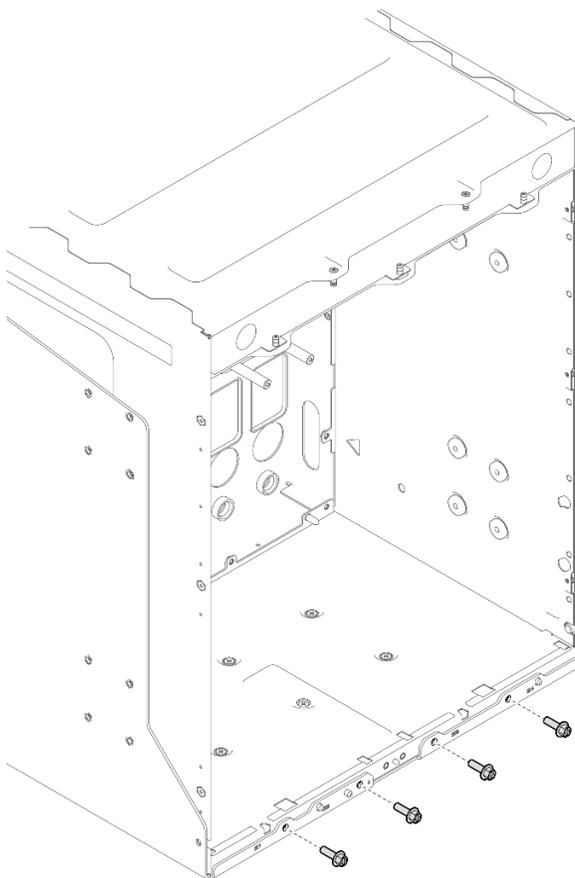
Retrait du support arrière de l'extrémité arrière du boîtier
